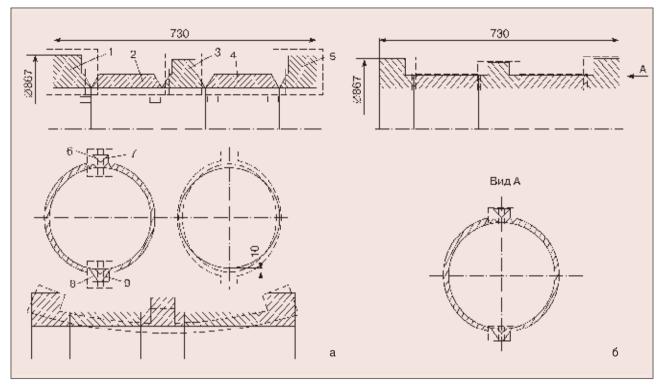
Корпус ротора 080028007 из сплава ЭП609 с толщиной стенки 30 мм (пунктиром показаны заготовки деталей под сварку и деформации узла после аргонодуговой сварки): а — вариант с аргонодуговой сваркой, б — вариант с электронно-лучевой сваркой
